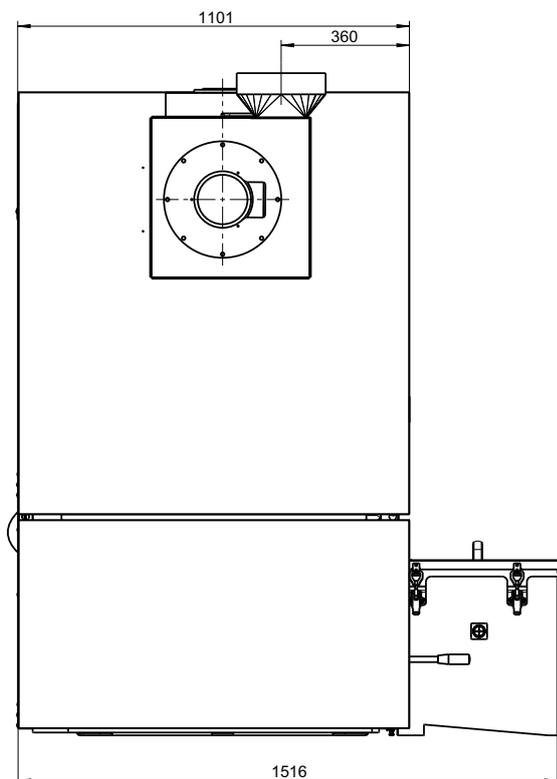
/3 - Dimensions à l'arrière HDG M175 - 240
